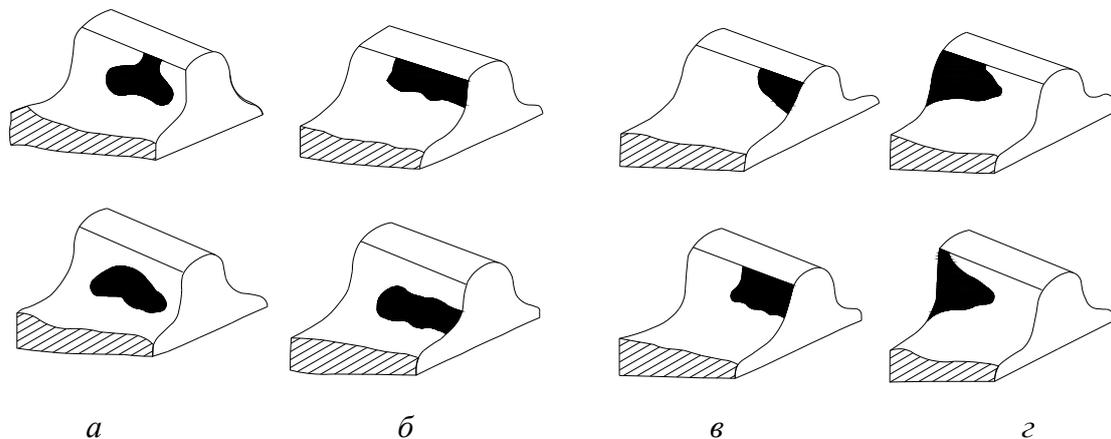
Расположение пятен контакта при проверке зацепления конических зубчатых колес на краску: верхний ряд – зубья ведущего колеса, нижний ряд – зубья ведомого колеса; *a* – пятно контакта при правильном зацеплении; *б, в, г* – пятна контакта при неправильном зацеплении
